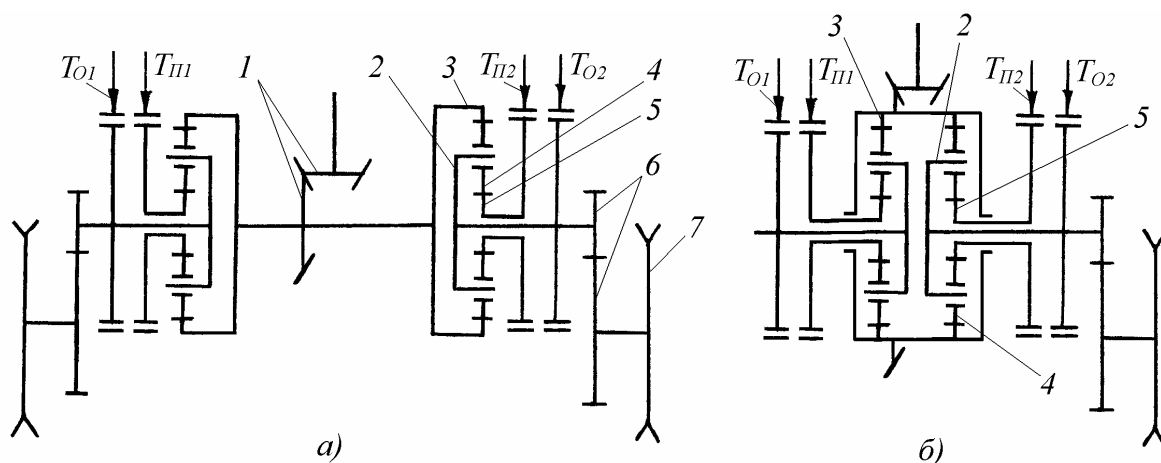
Одноступенчатый планетарный механизм поворота:
